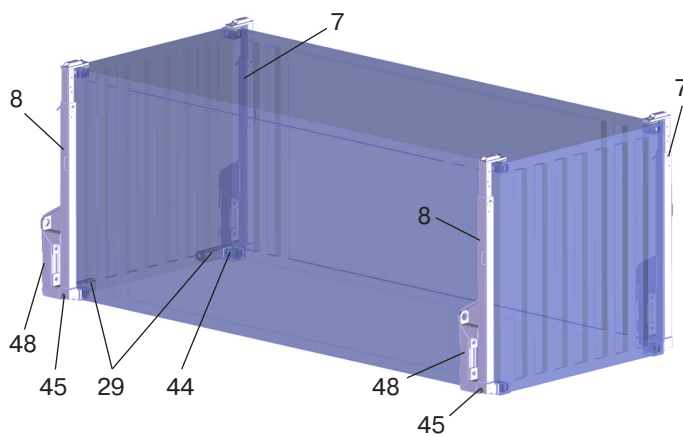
Ladebetrieb ‚Horizontale Rampe‘
